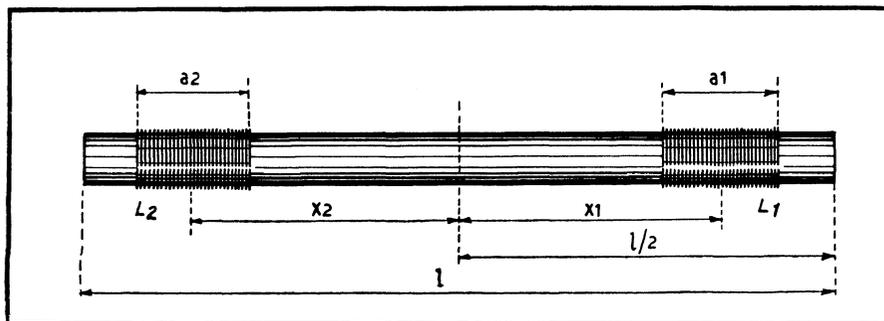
Dimensions à considérer dans le cas de deux bobines.
